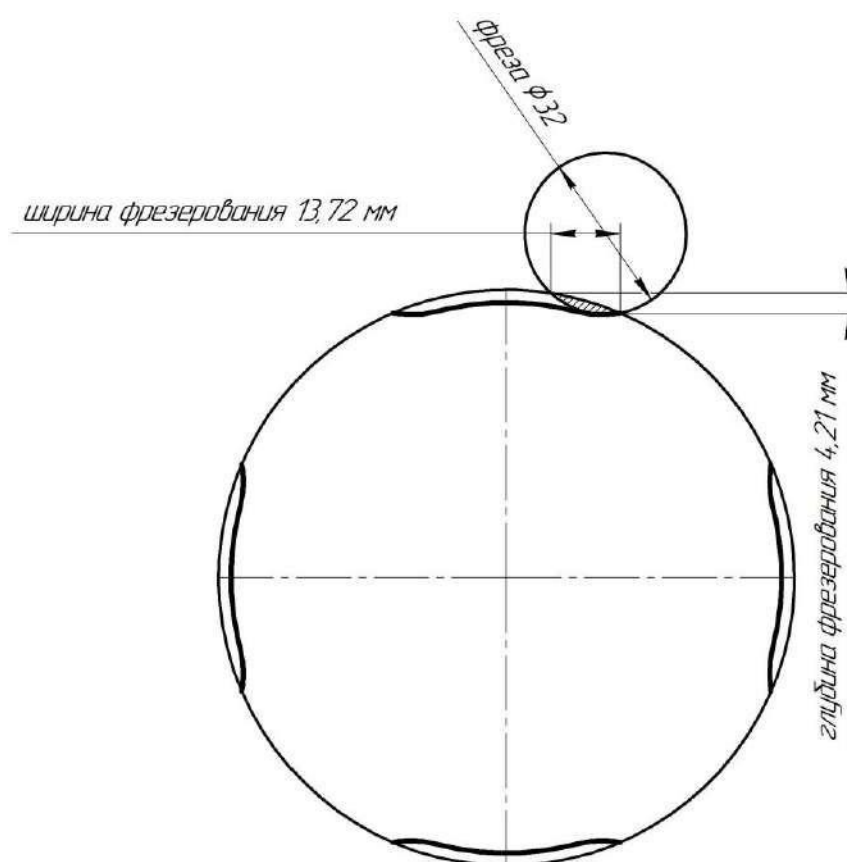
Параметры фрезерования фасонной поверхности
